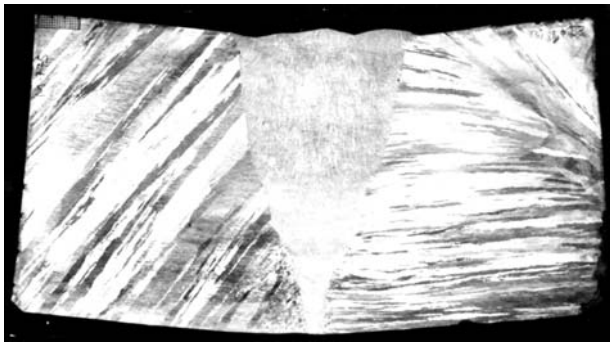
Сварной шов на электрошлаковой литой криогенной аустенитной стали 12Х18Н10ТШ-Л (толщиной 110 мм), выполненный автоматической сваркой под флюсом
